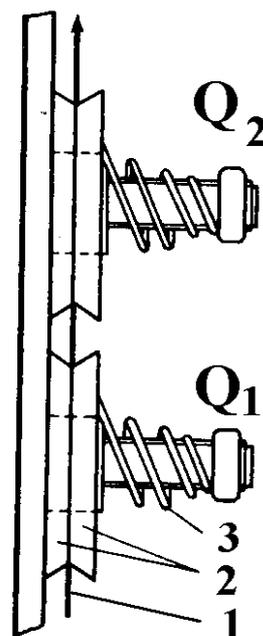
Двухзонный дисковый нитенатяжитель
